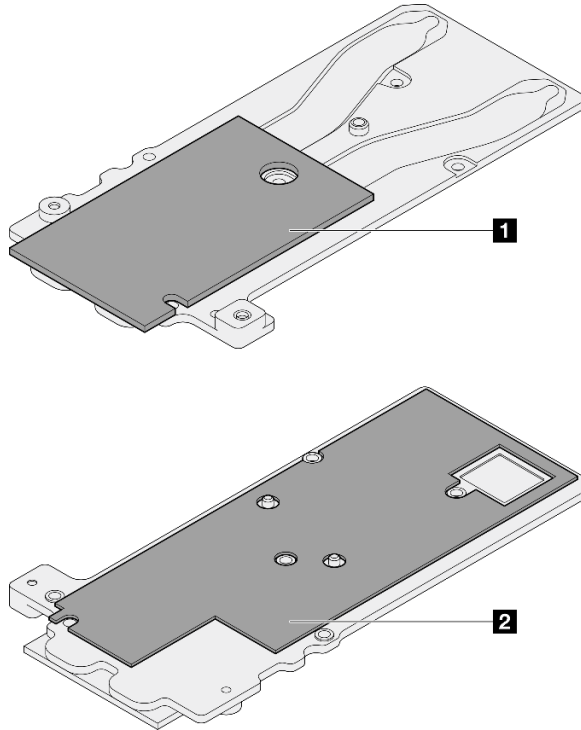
Remplacement des tampons de mastic de la plaque de conduction du module OSFP
